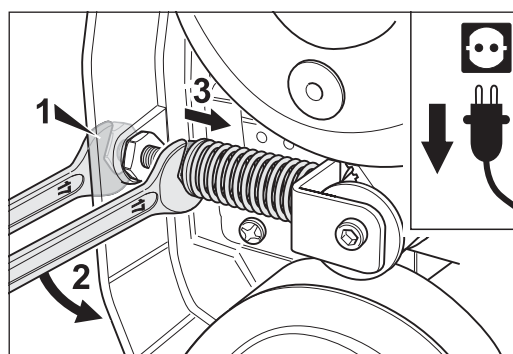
Die Schraube des Zahnriemenspanners mit einem Gabelschlüssel festhalten (1) und gleichzeitig mit einem zweiten Gabelschlüssel die Spannmutter gegen die Feder schrauben (2 + 3).
